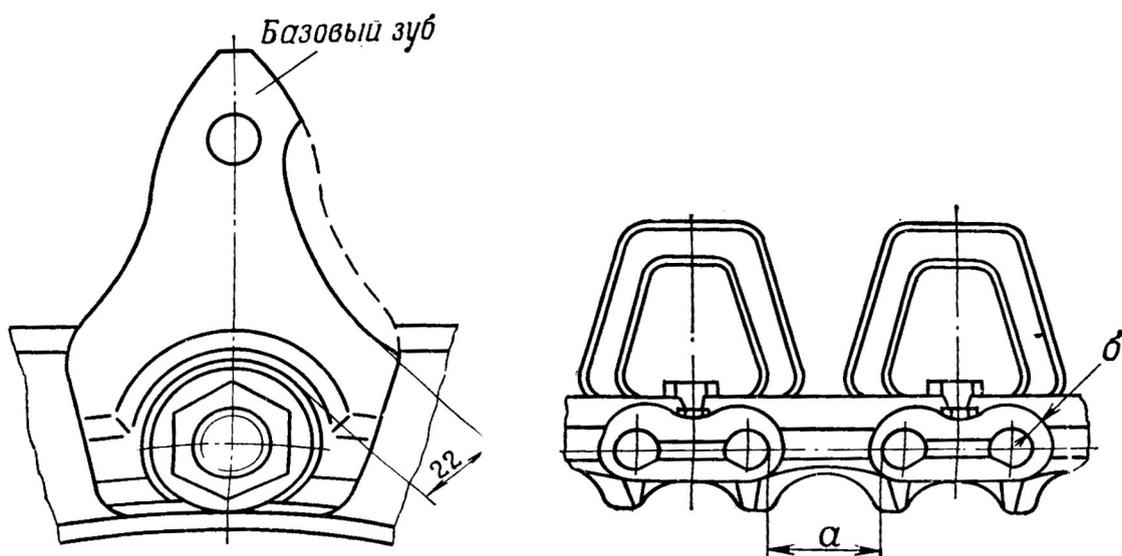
Предельный износ зубьев ведущего колеса, РМШ и скобы
